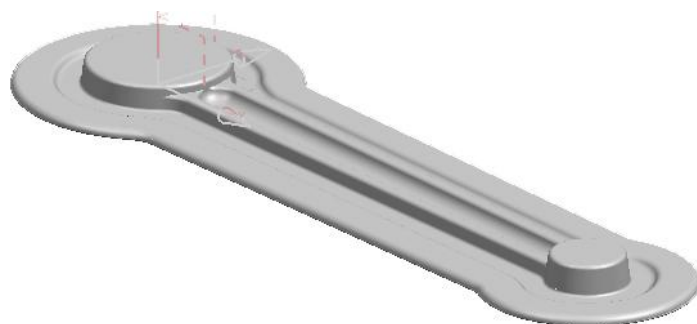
Поковка "шатун" после штамповки в окончательном ручье.
